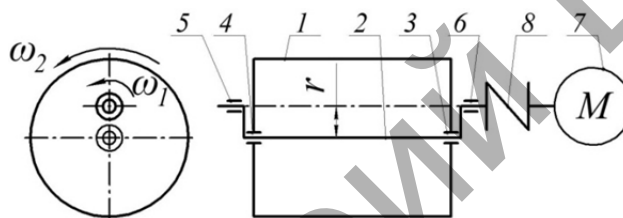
Схема эксцентрикового вала вибровалкового измельчителя
